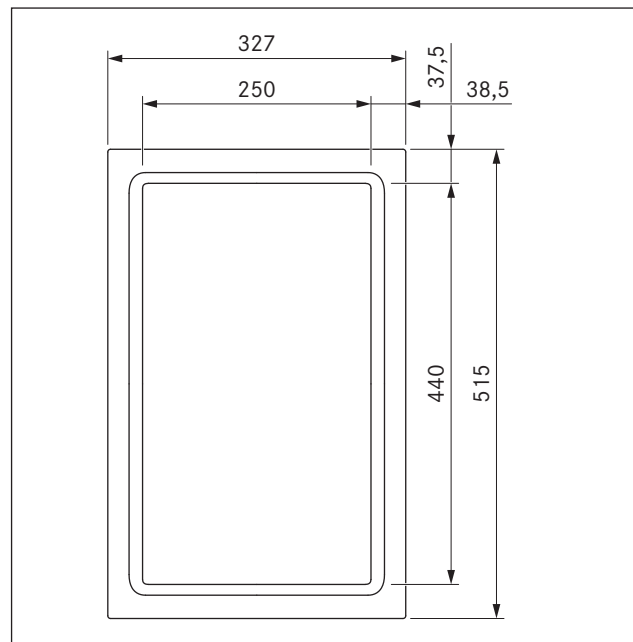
CKT apparatets dimensjoner sett ovenfra
